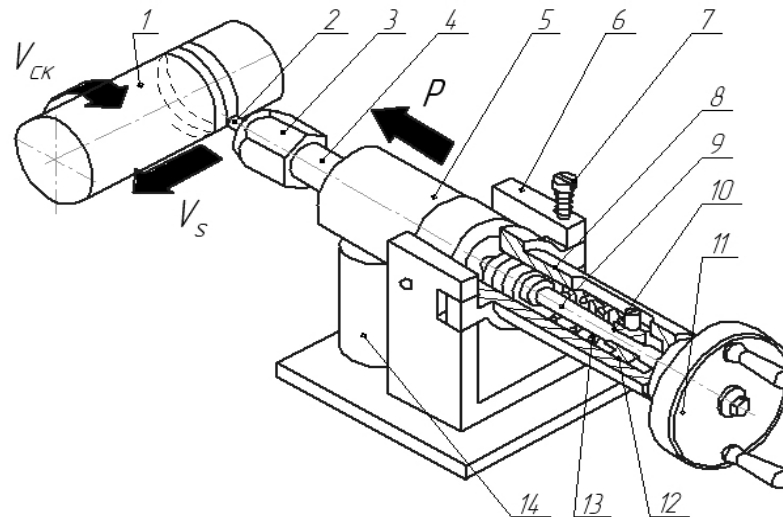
Схема работы моделирующей установки. 1 – индентор, 2 – контртело, 3 – гайка, 4 – шток, 5 – корпус штока, 6 – стойка, 7 – зажим, 8 – корпус зажимного устройства, 9 – толкатель, 10 – вал, 11 – диск, 12 – ползун, 13 – пружина, 14 – датчик давления.
